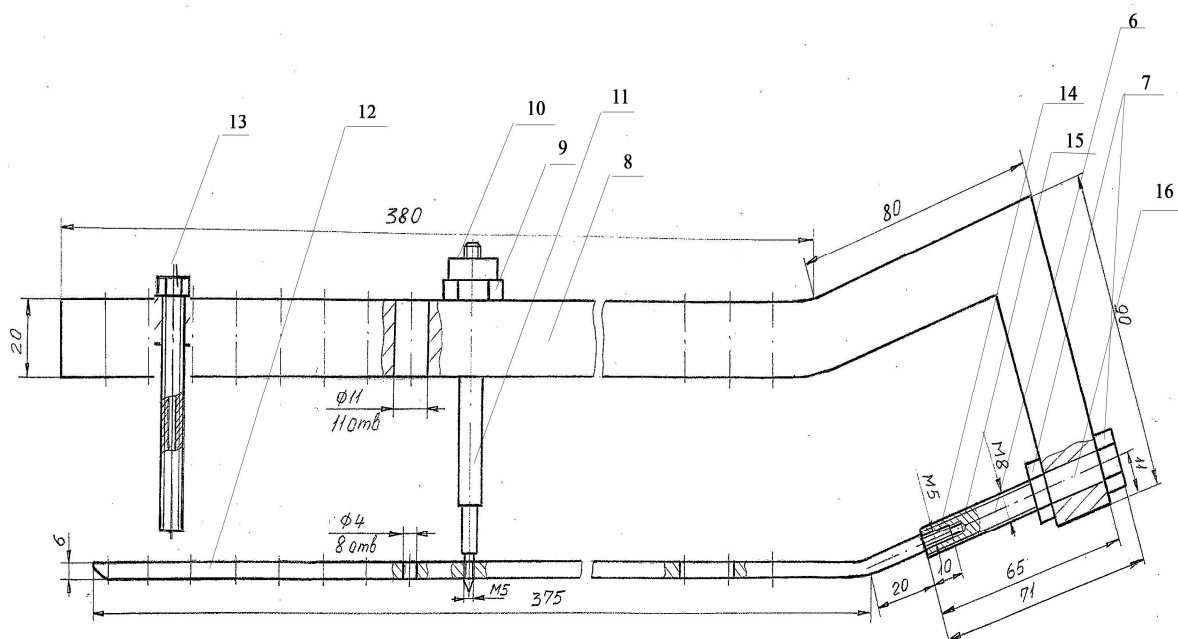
Устройство для интрамедуллярного остеосинтеза большеберцовой кости с блокированием винтами: 6 – проксимальный контактор; 7 – гайки резьбового наконечника проксимального контактора; 8 – направляющая планка с отверстиями; 9 – фиксирующая втулка дистального контактора; 10 – гайка дистального контактора; 11 – дистальной контактор; 12 – стержень; 13 – втулка для сверления.
